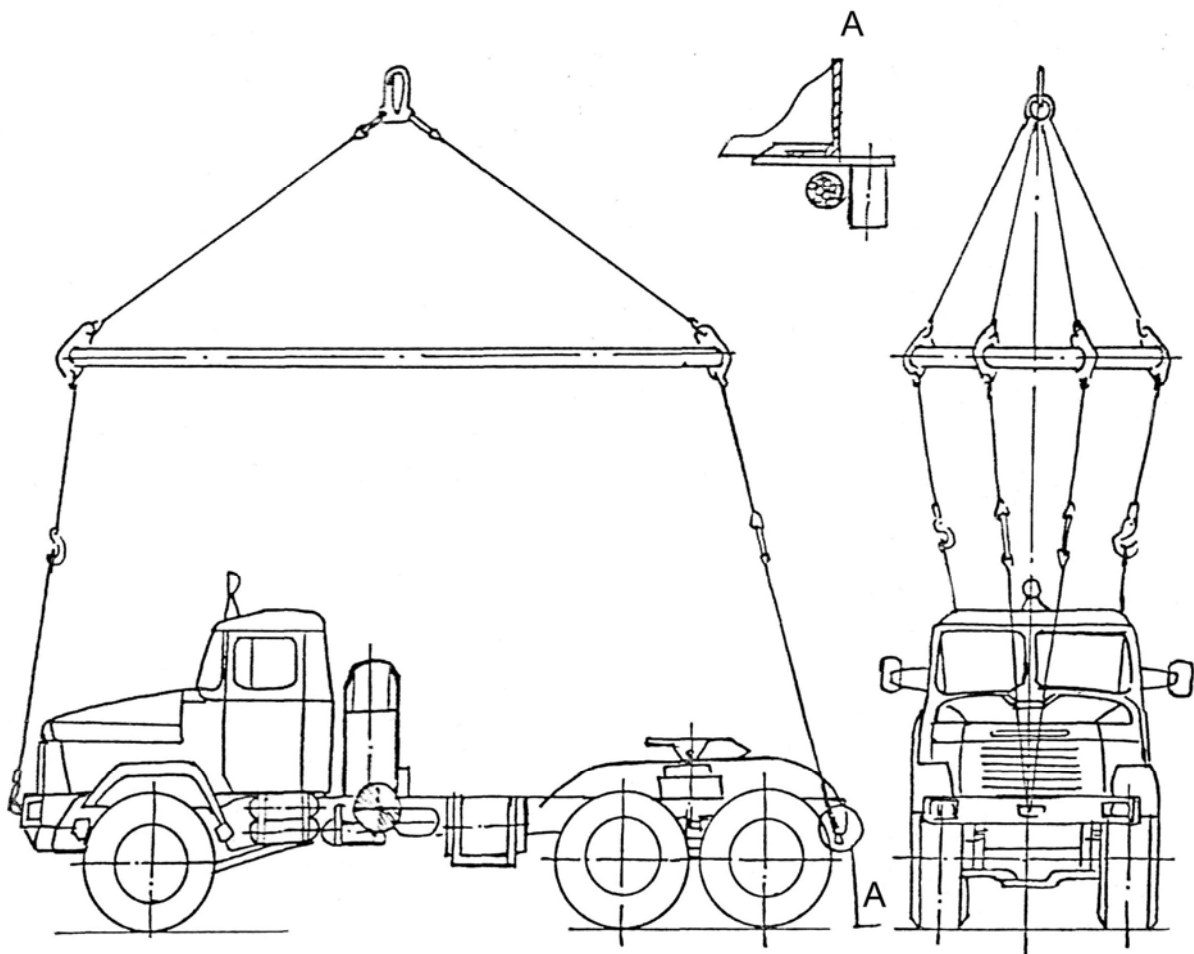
Схема строповки автомобиля КрАЗ-6446-02
